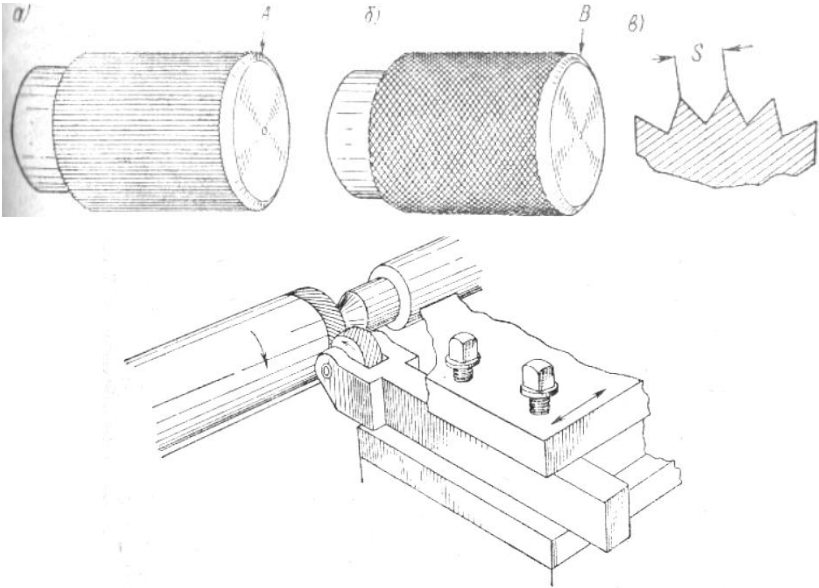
Накатка рифлений на цилиндрических поверхностях: а-прямая; б-косая; в- шаг накатки; закрепление накатного приспособления(державки) в резцедержателе станка
